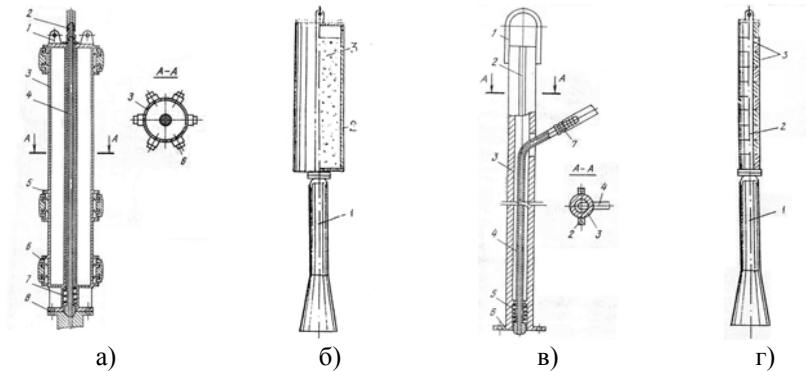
Конструкции штанг фурменных устройств разных конструкций:
